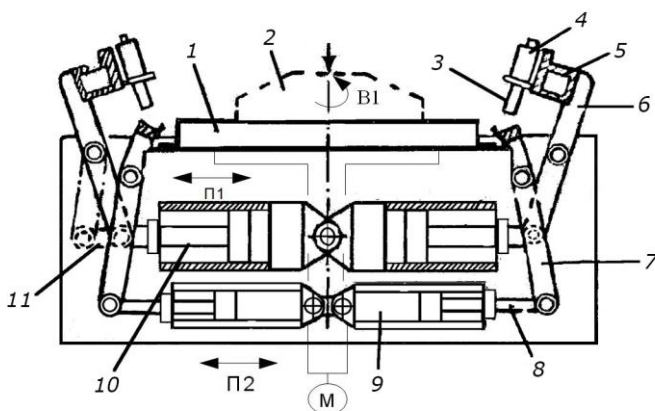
Сварочный автомат: 1 – изготавливаемое изделие; 2 – прижим; 3 – электроды; 4 – штампы; 5 – сварочные пистолеты; 6 – отжимные балки; 7 – поджимные балки; 8 и 11 – рычаги; 9 и 10 – гидроцилиндры
